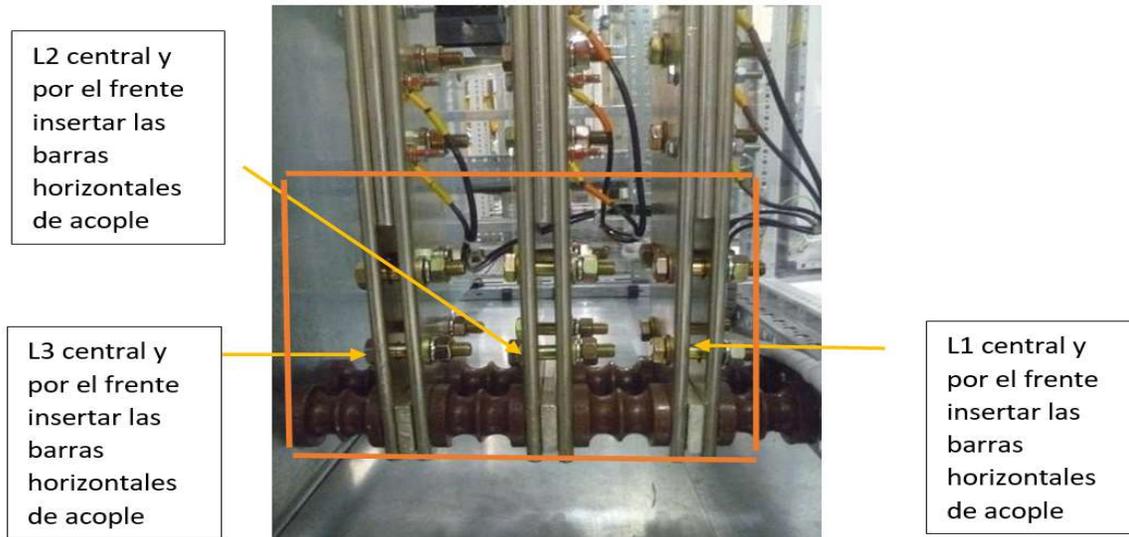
Disposición de las barras verticales en el tablero de distribución
